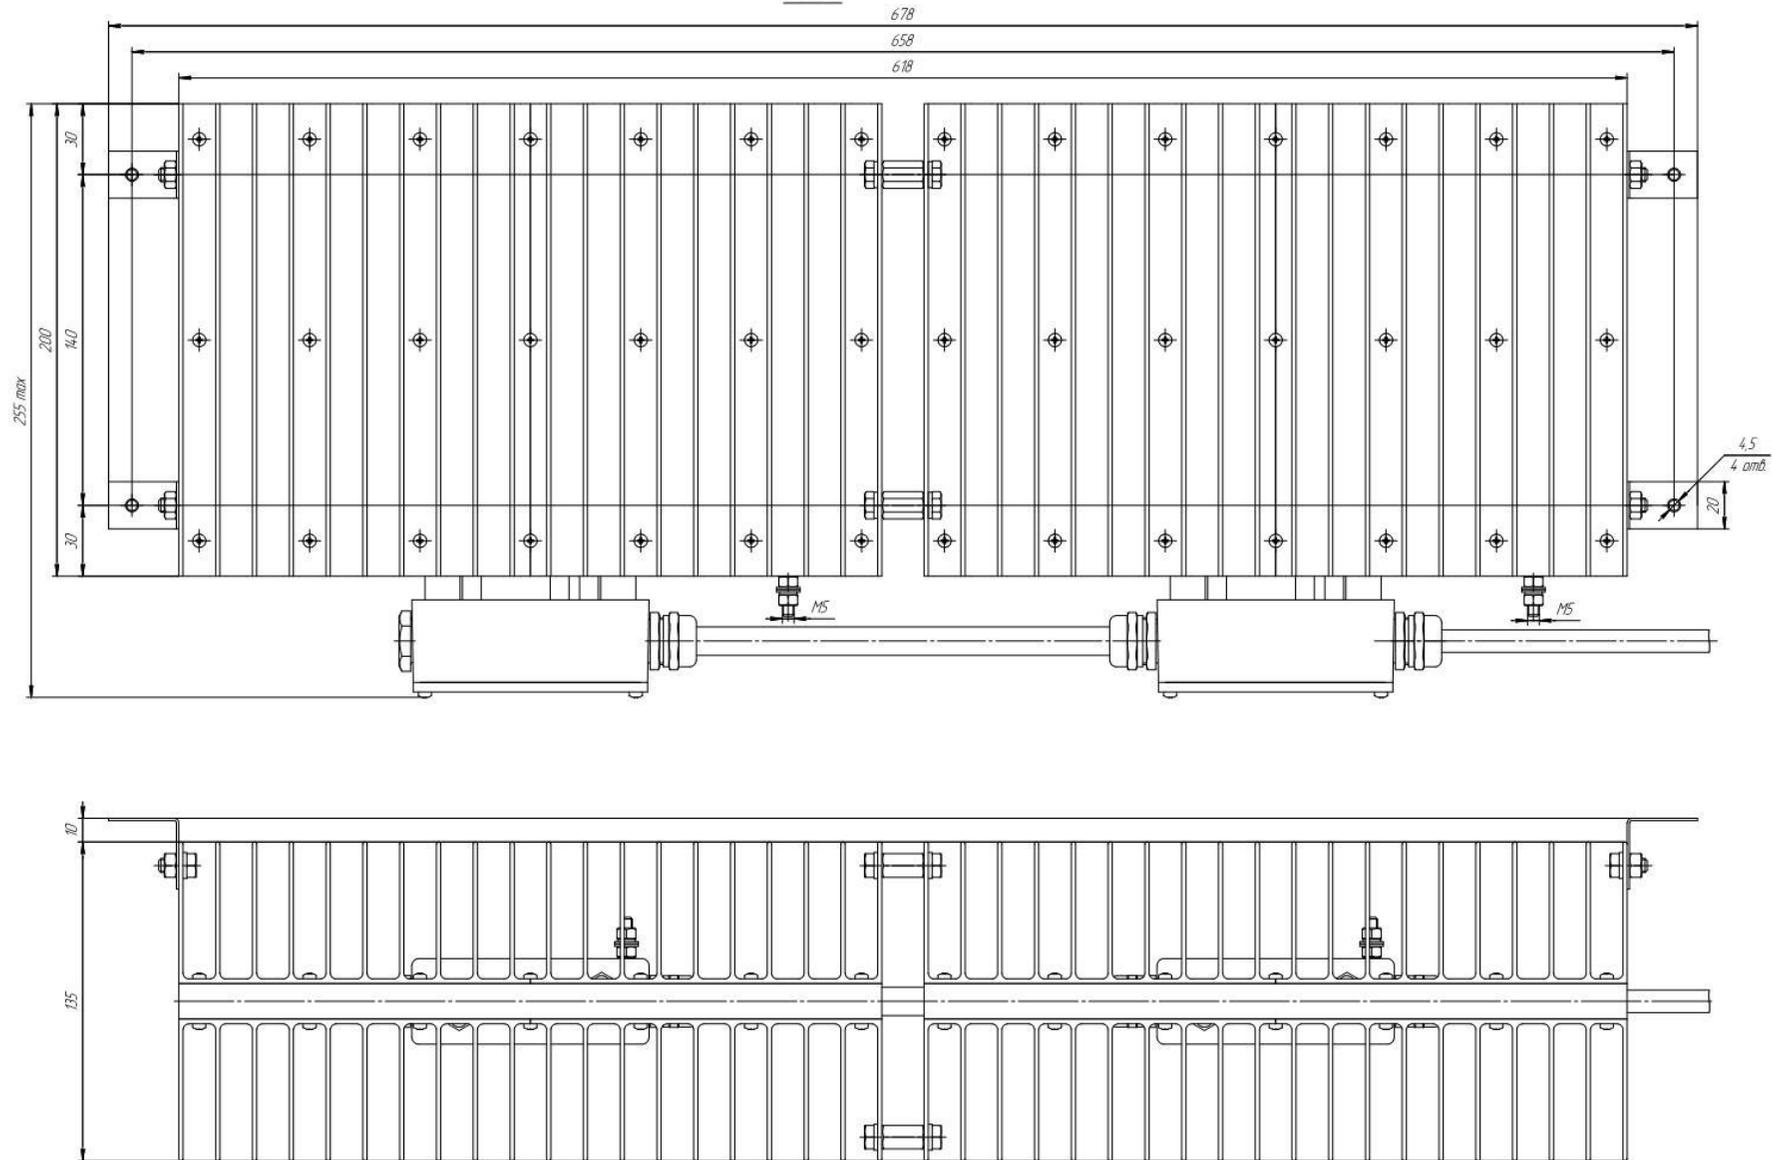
Присоединительные размеры для исполнения ОВР-3000
